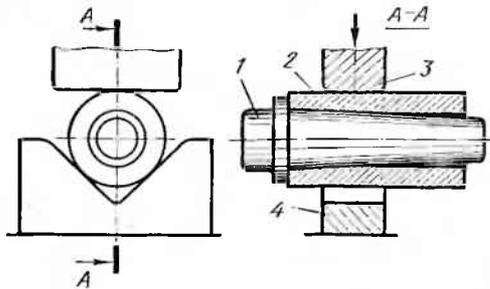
Схема протяжки с оправкой: 1 — оправка (отверстие для охлаждения не показано), 2 — заготовка, 3 — верхний боек, 4 — нижний вырезной боек
